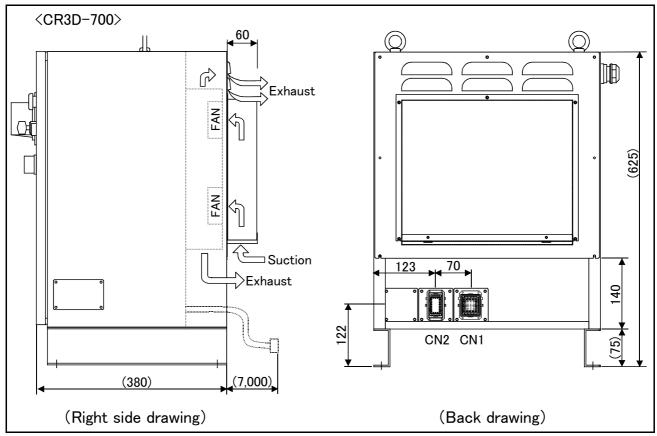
Outside dimensions of controller (CR3D-700 Supplement)
